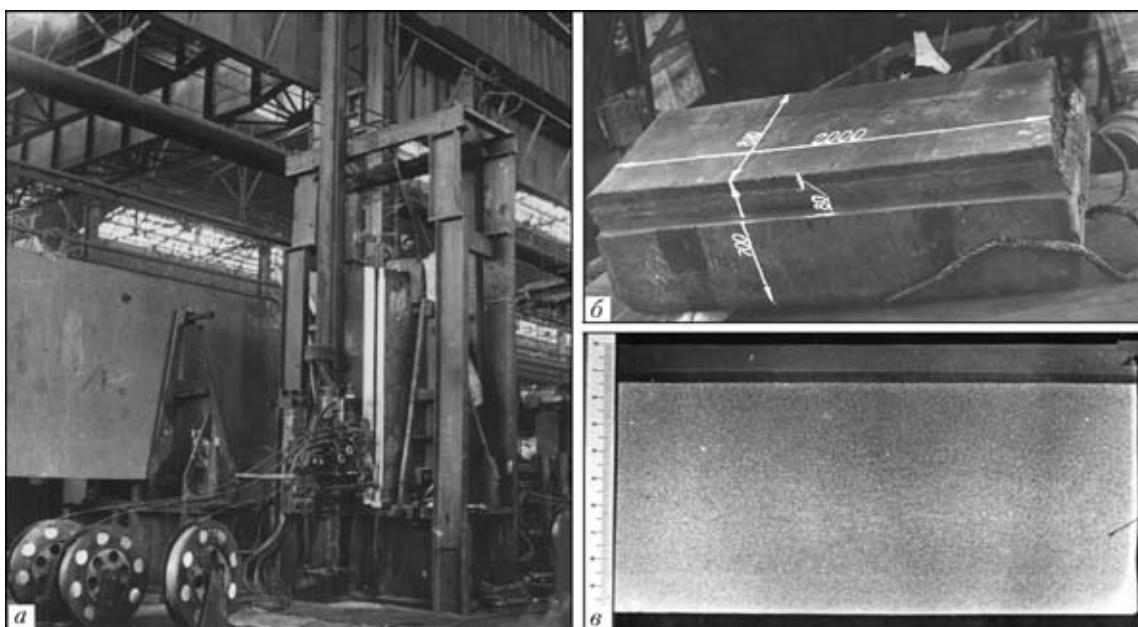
Двухслойная заготовка, подготовленная к ЭШС с применением электродов (6 шт.) двумя аппаратами А-535 одновременно в общую сварочную ванну (а), двухслойная заготовка после ЭШС (б) и макрошлиф биметалла 09Г2ДТ + 1Х18Н10Т ($\delta = 100$ мм), прокатанного из указанной двухслойной заготовки (в)
